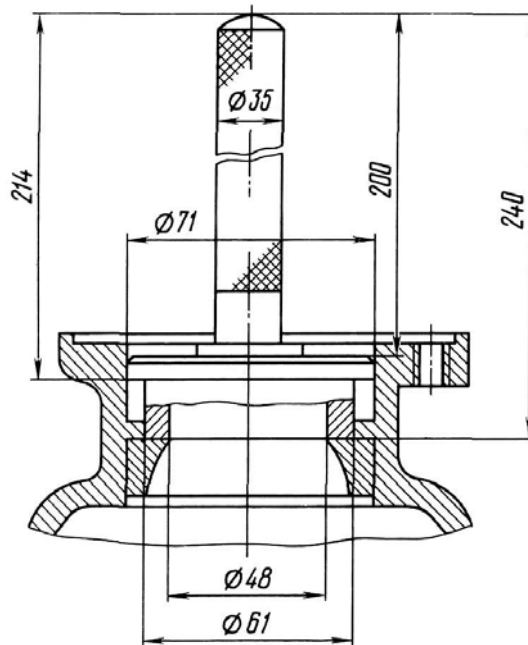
Выпрессовка наружной обоймы сферического подшипника
